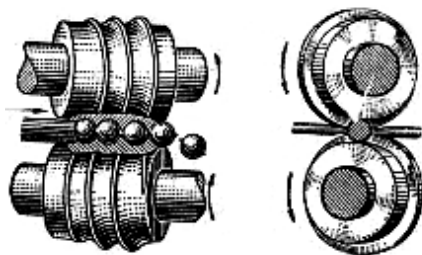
Схема поперечно-винтовой прокатки шаров
